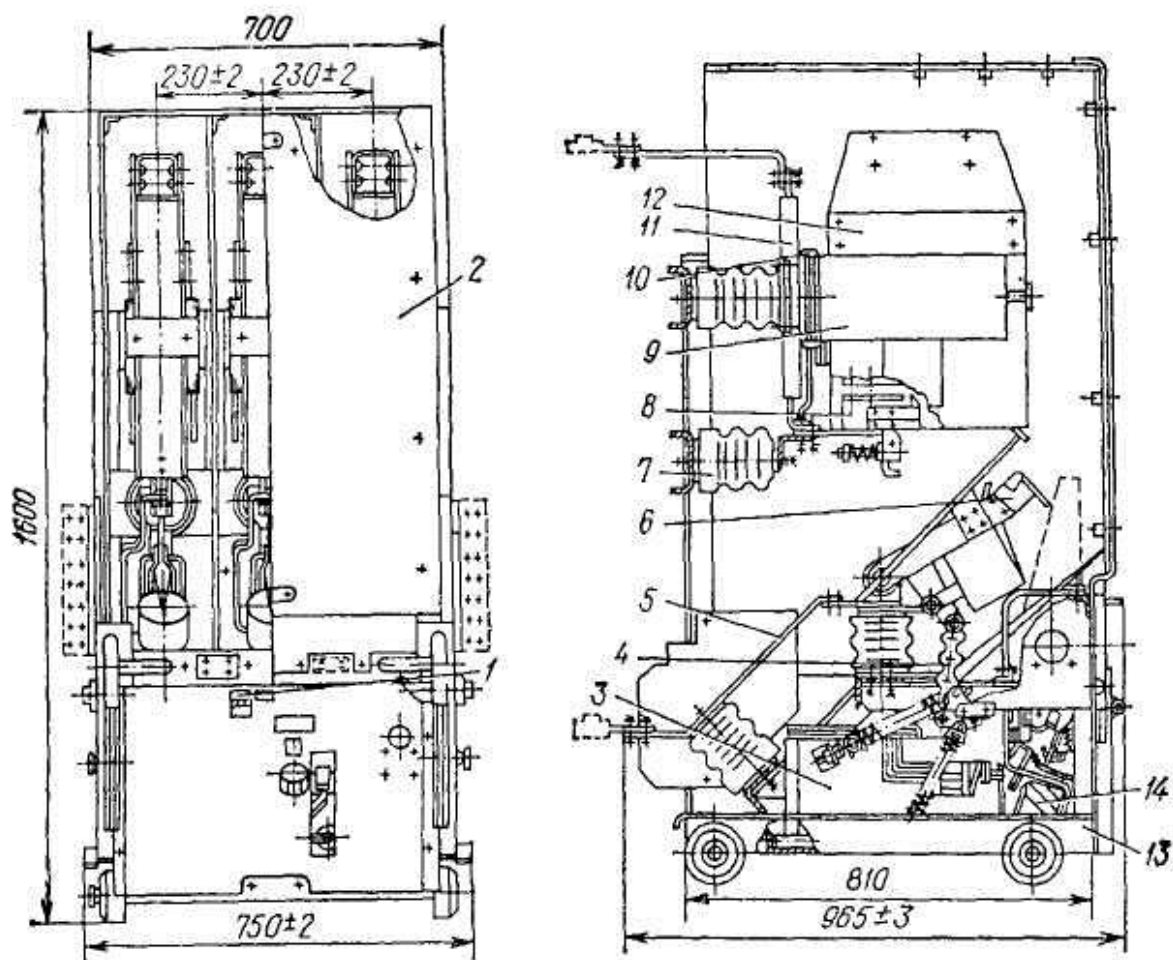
Выключатель типа ВЭМ-10Э-1000/12,5-У3:
